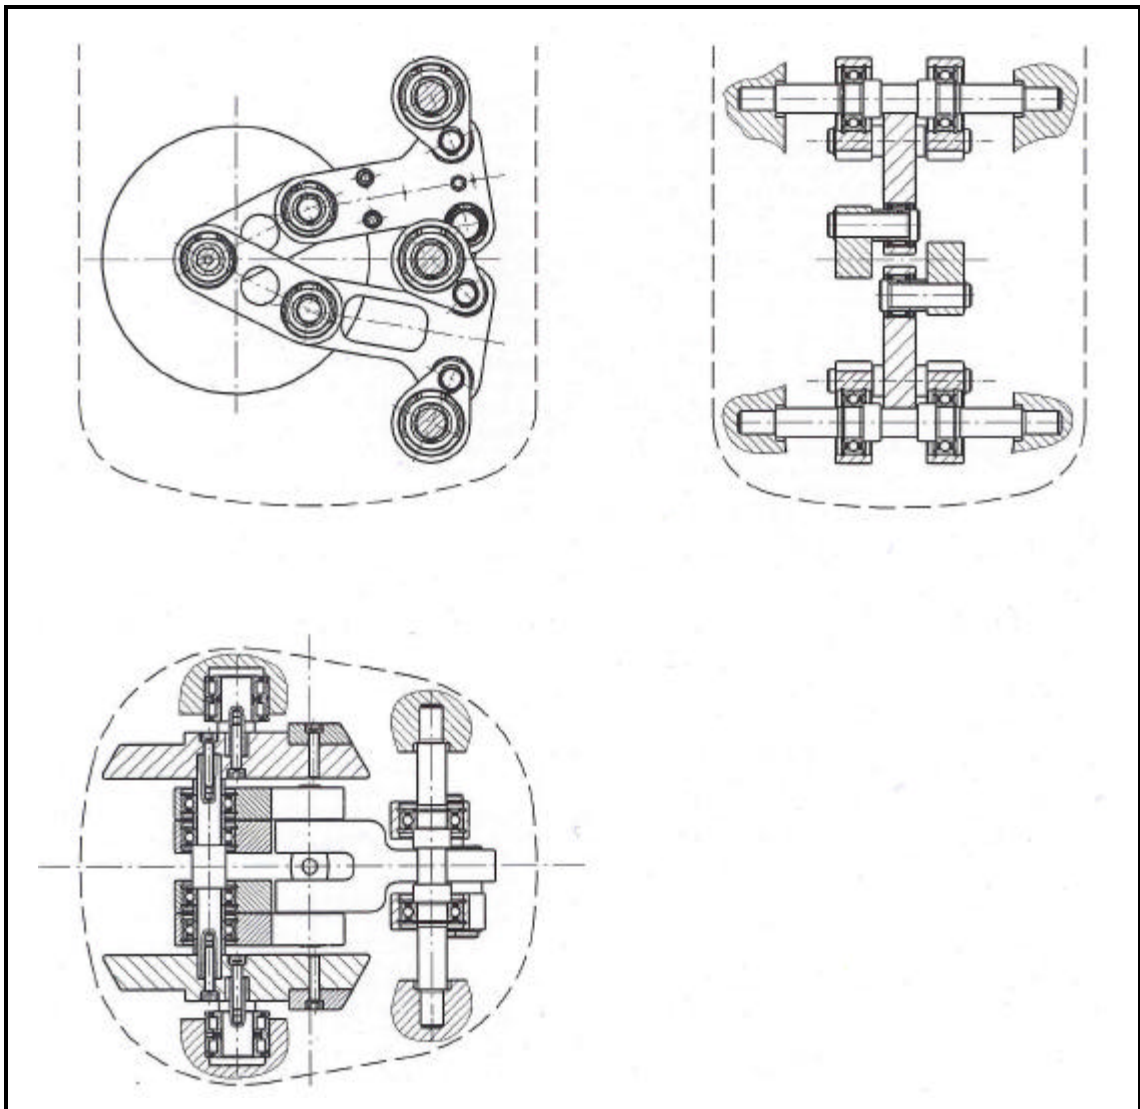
Gesamtzeichnung eines Getriebes für die 20 kW Vuilleumier-Wärmepumpe auf der Basis des Roberts'schen Dreieckslenkers
